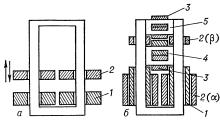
Схема сварочного трансформатора для дуговой сварки: a-c механическим регулированием индуктивного сопротиврегулированием индуктивного сопротны-ления и напряжения; 6 — с электрическим регулированием; 1 и 2 — первичная и вторичная обмотки; 3 — обмотка управ-ления; 4 и 5 — среднее и верхнее ярмо.
